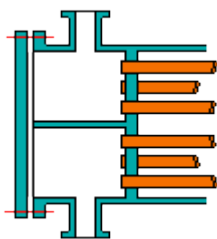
Cabezal frontal con placa de tubos y cubierta removible (tipo N)
